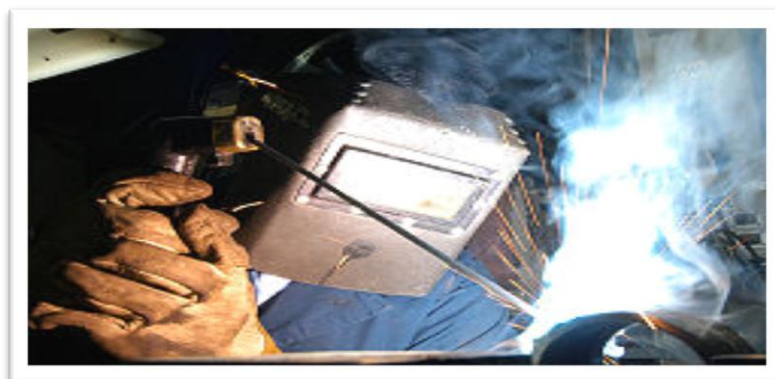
Distintos Sistemas de Soldadura
